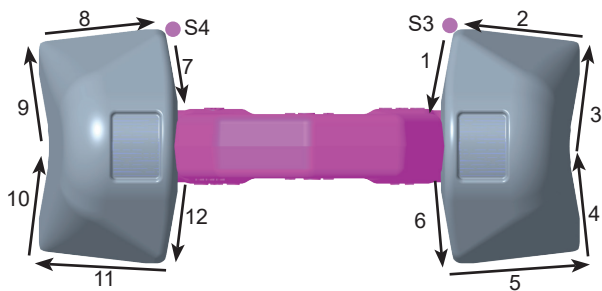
последовательность сварки верхнего шва (S = начальная точка)
